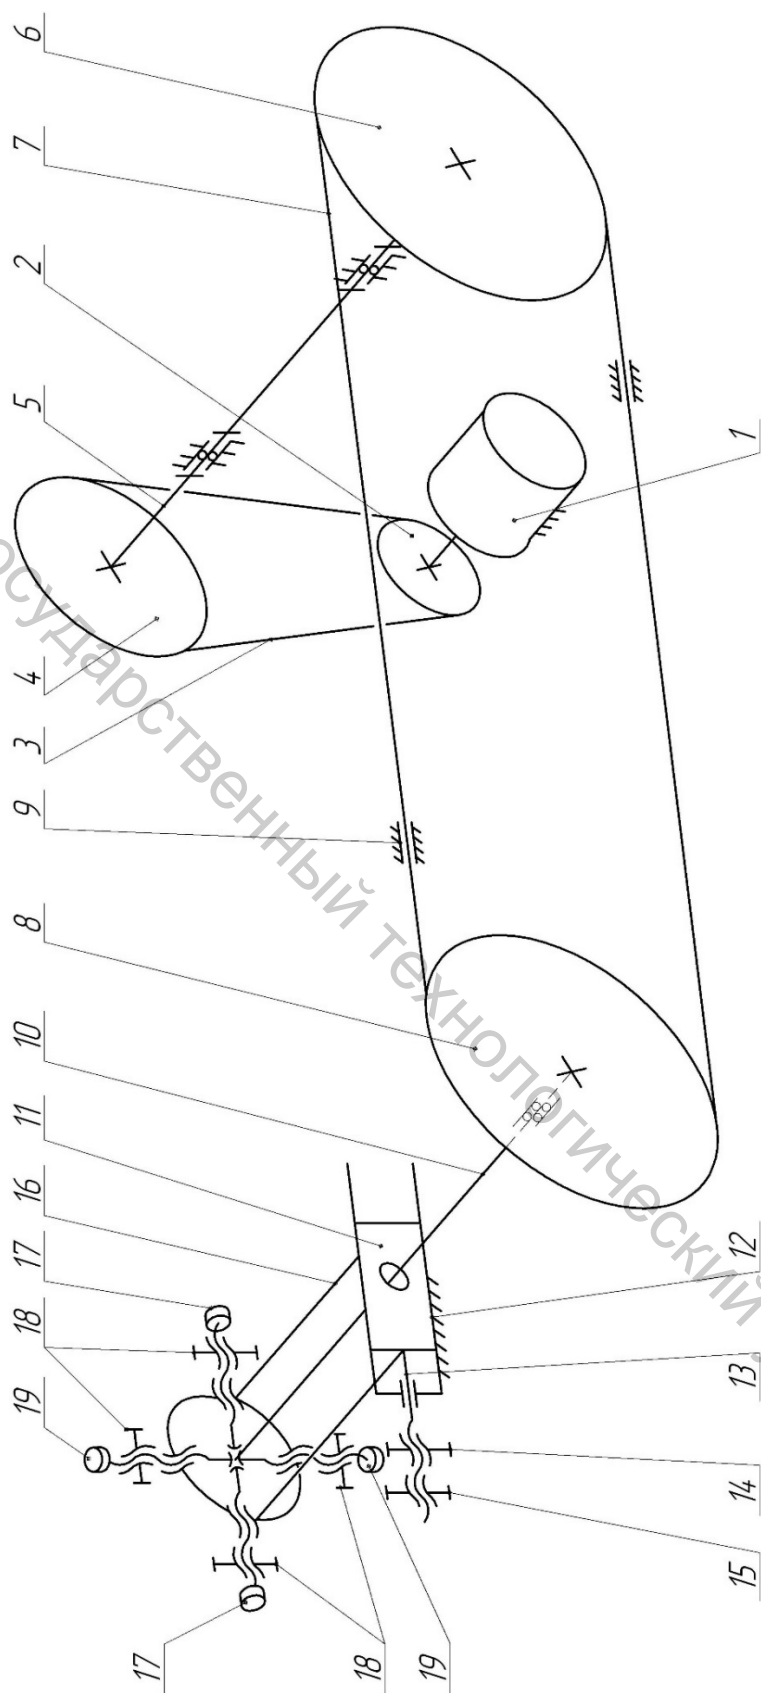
Кинематическая схема механизма ленточного ножа
